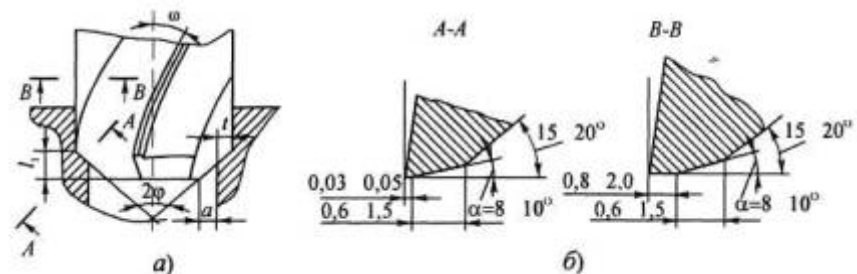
Режущая часть зенкера: а – элементы режущей части; б – формы заточки зубьев зенкера
